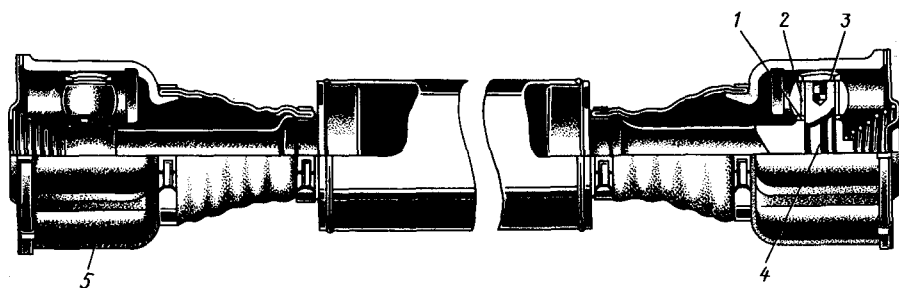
Карданный вал с двумя универсальными шарнирами.
